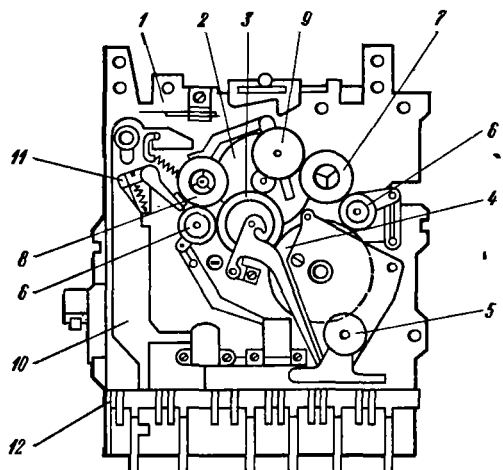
Внешний вид ЛПМ (вид сверху): 1 — шасси; 2 — электродвигатель; 3 — ролик привода ведущего вала; 4 — маховик (вал ведущий в сборе); 5 — прижимной ролик; 6 — ролик перемотки; 7 — подкассетный (приемный) узел; 8 — подкассетный (подающий) узел; 9 — ролик подмотки; 10 — ползун воспроизведения; 11 — рычаг подмагничивания; 12 — клавишная станция
